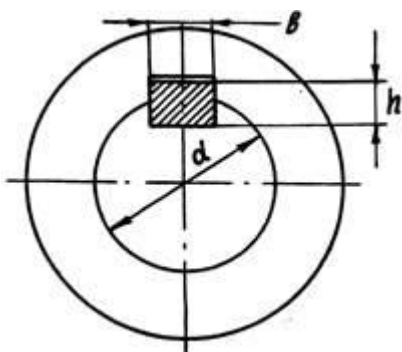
Конструкція шпонкового з'єднання з призматичною шпонкою
